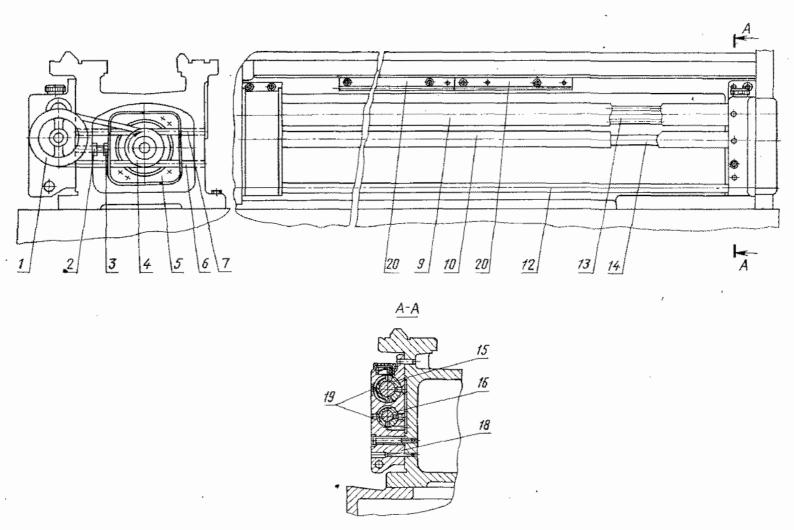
Станина, рейки, ходовой винт, ходовой вал и привод быстрых перемещений суппорта
